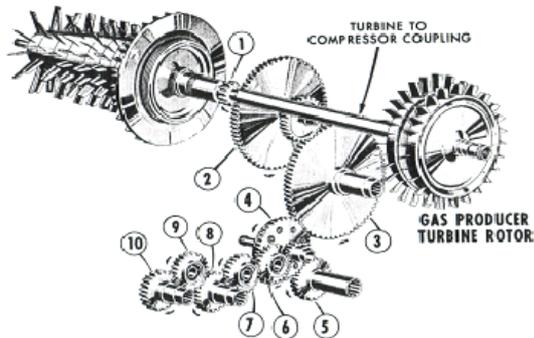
Tren de engranajes de la turbina generadora de gas.
